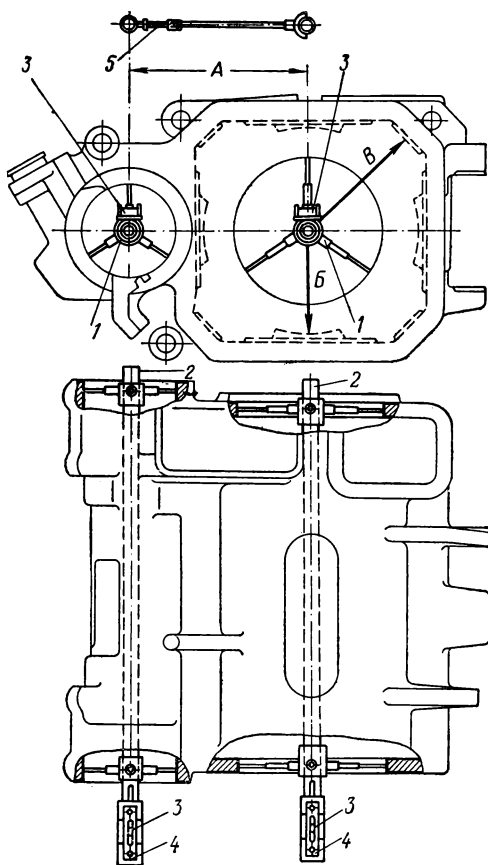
Приспособления для проверки расточки остова под щиты и моторно-осевые подшипники:
